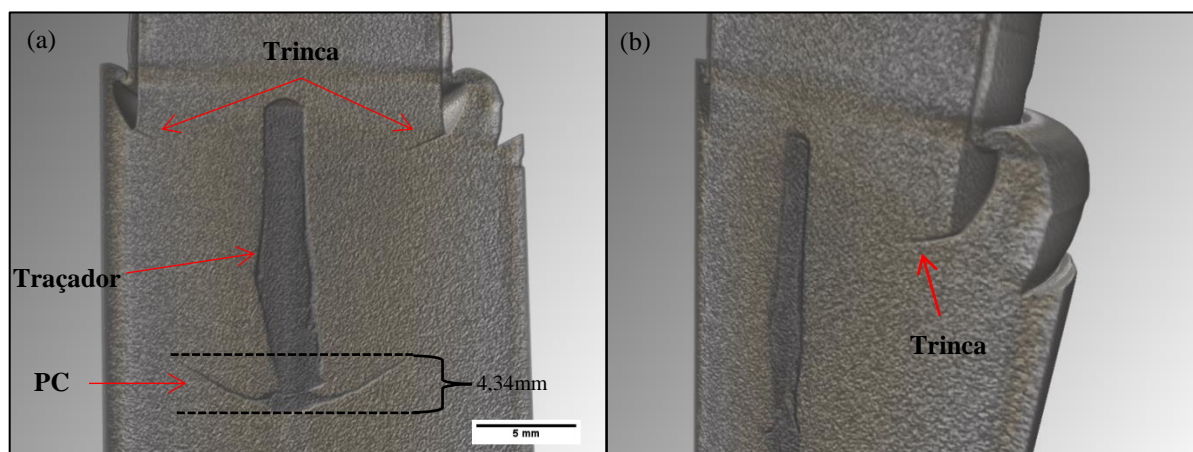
Vista do corte transversal frontal (a) e vista do corte transversal frontal rotacionada (b) do volume 3D da solda 07.
